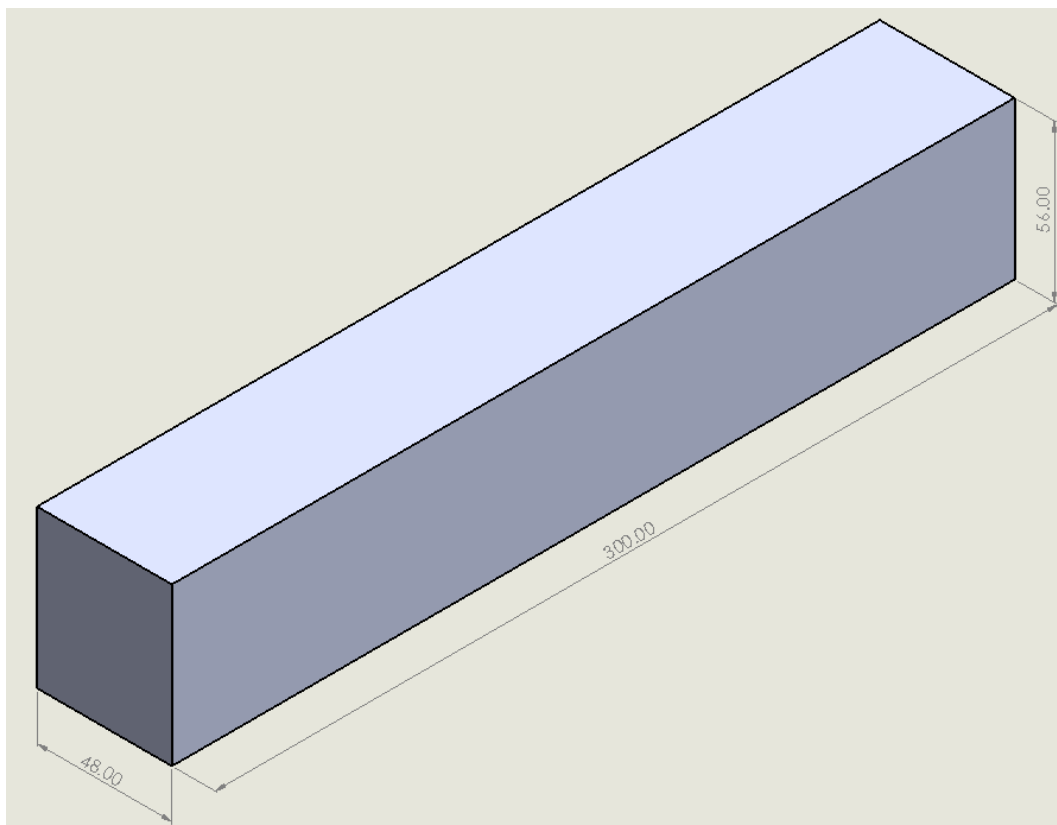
Dimensionamiento de la probeta para los ensayos en la fresadora CNC.
